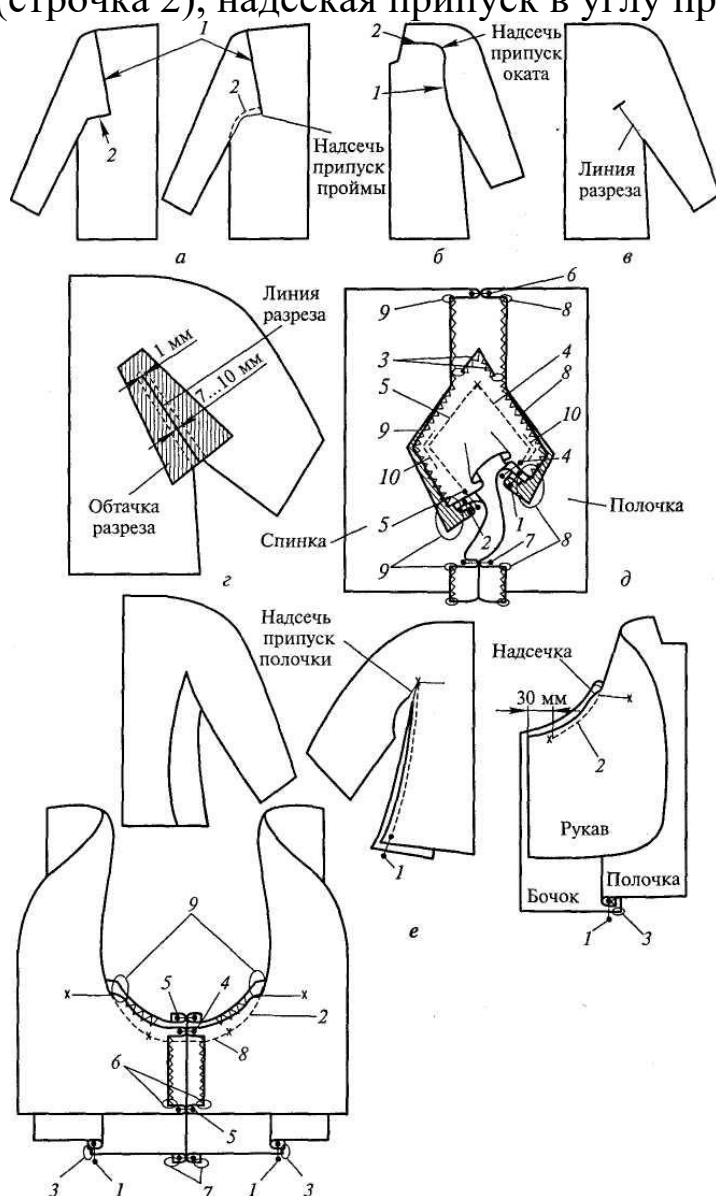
Методы обработки и сборки рукавов различной конструкции
